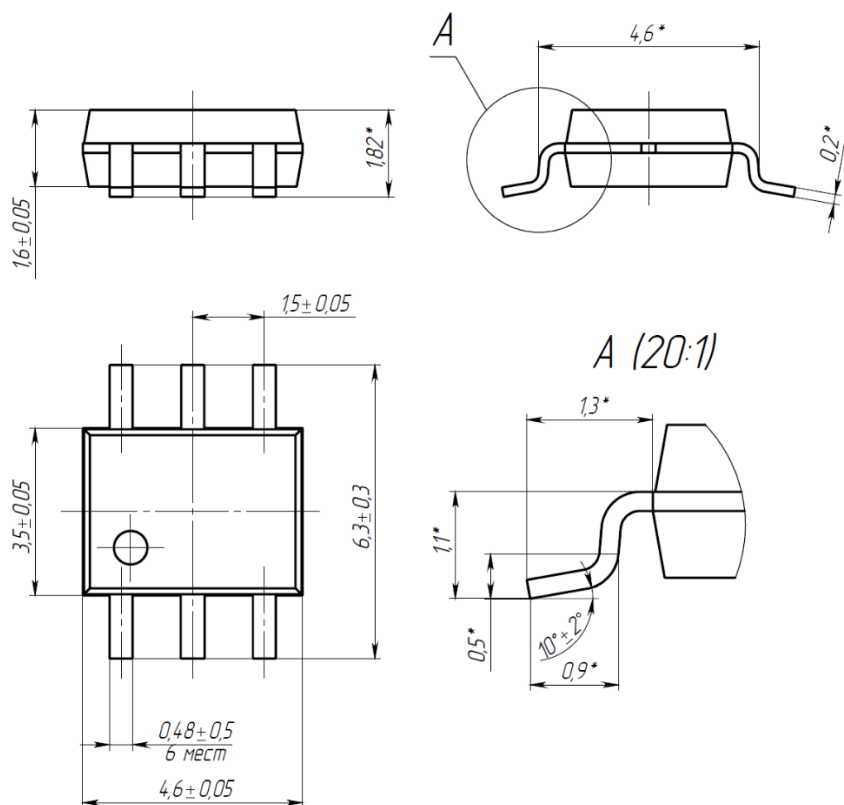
Габаритный чертеж корпуса 4341.6-1 К (размеры в мм)
